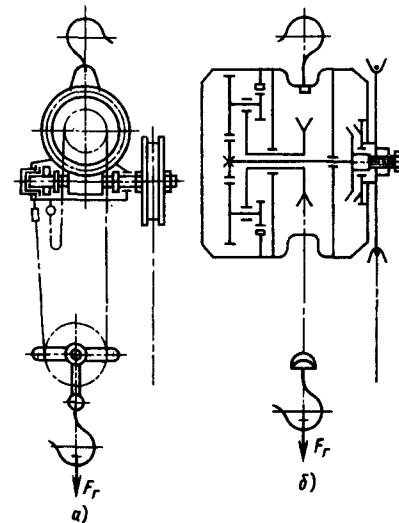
Схемы талей с ручным приводом: а — червячная; б — шестеренчатая
